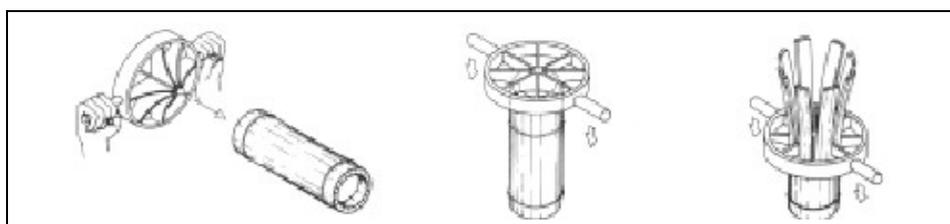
Corte do Bambu em tiras com faca múltiplo corte
